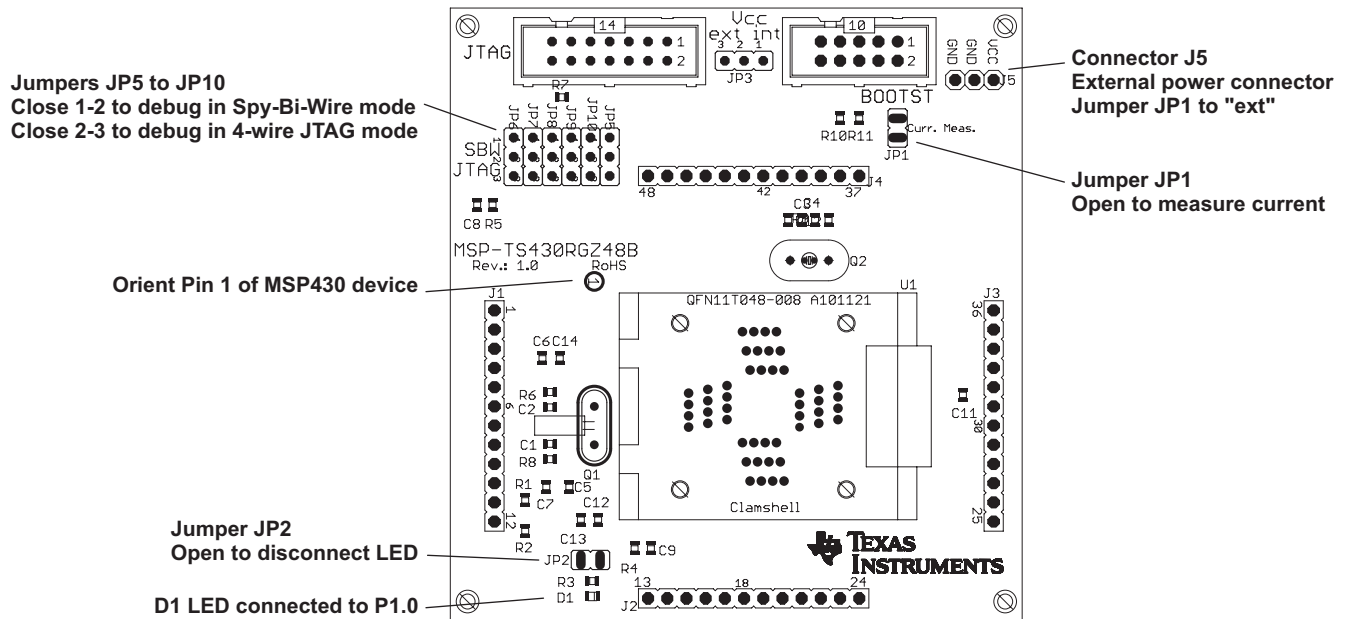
MSP-TS430RRGZ48B 目标插座模块, PCB
